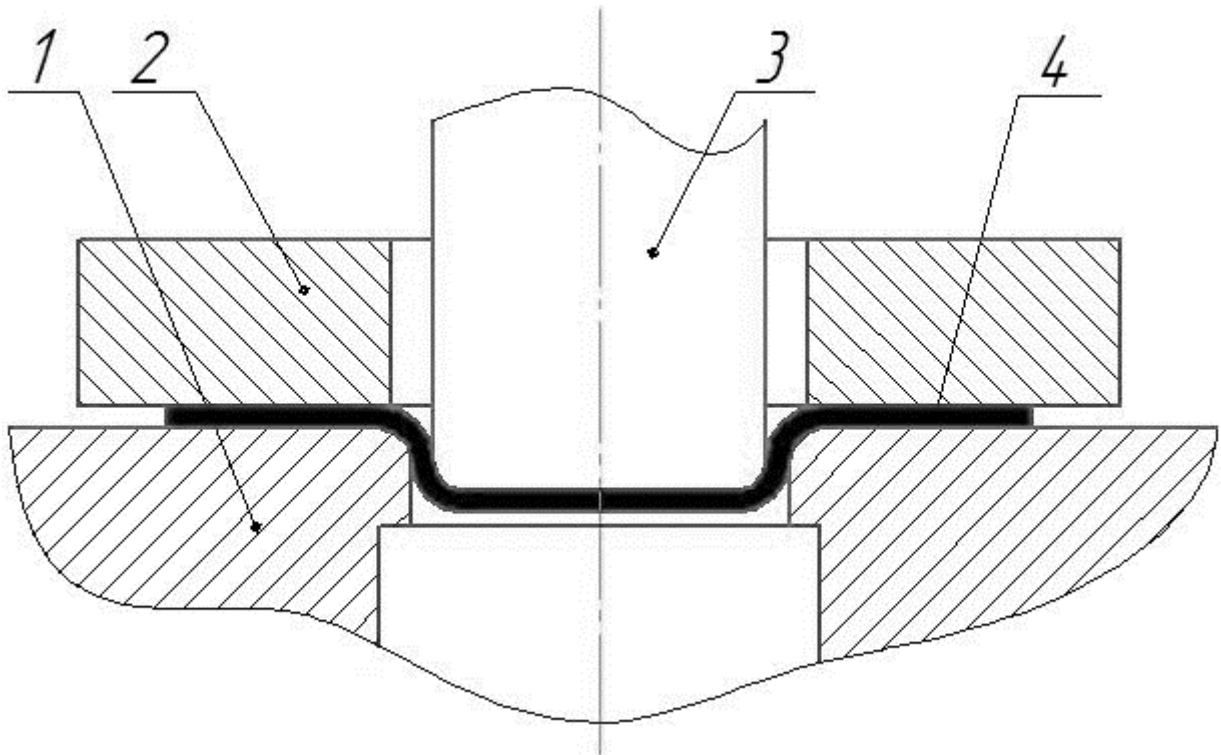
Схема вытяжки с прижимом: 1 – матрица; 2 – прижим; 3 – пуансон; 4 – заготовка.
